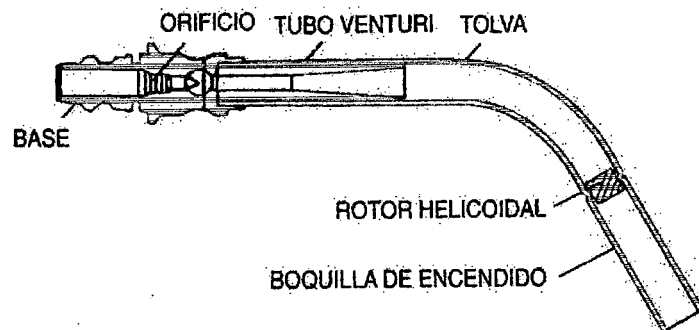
Mechero de propano con la típica boquilla de soldar
